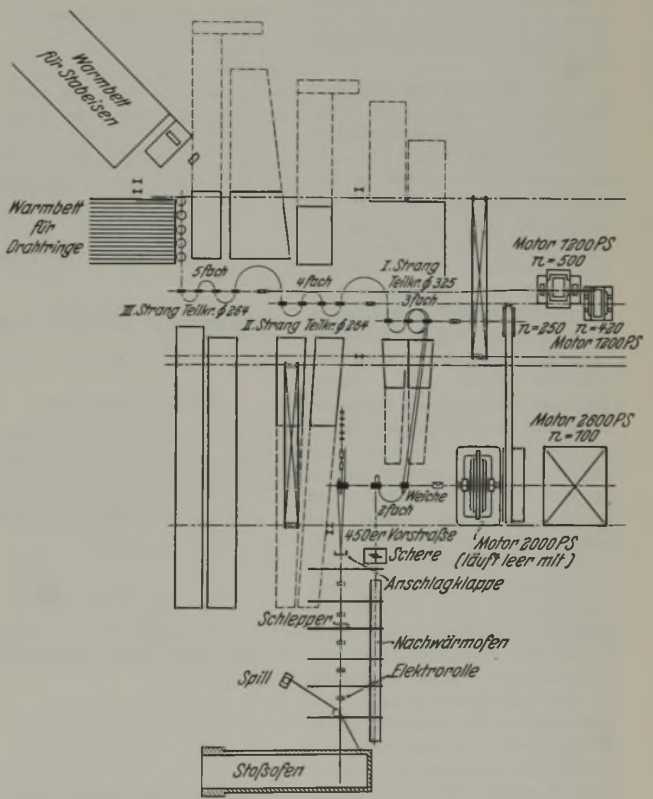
Lageplan der Drahtstraße im Jahre 1930.
